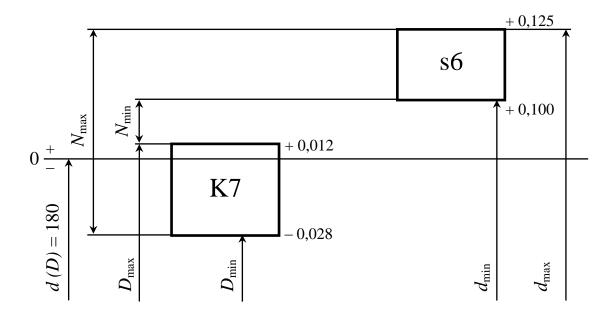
Схема расположения полей допусков соединения Ø160K7/s6
